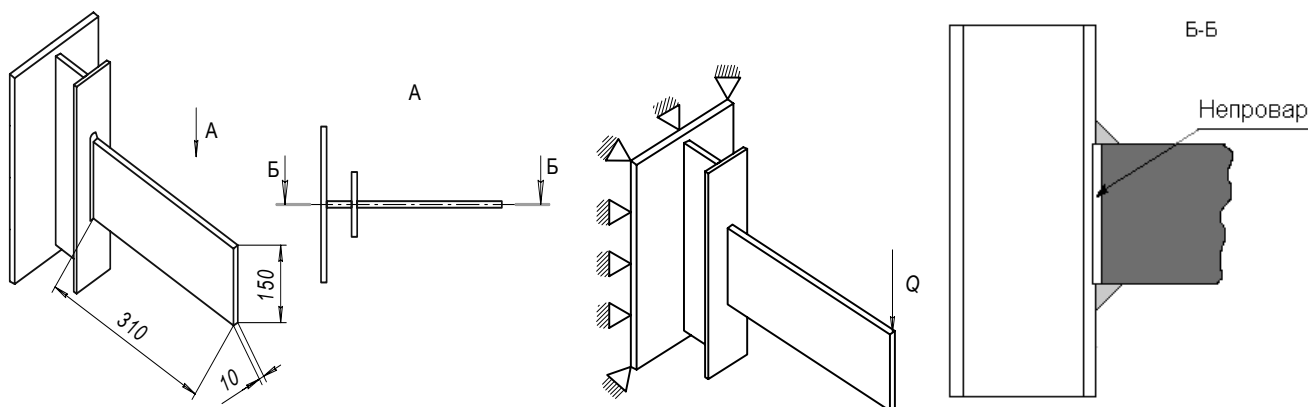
Эскиз сварного узла и схема его нагружения
